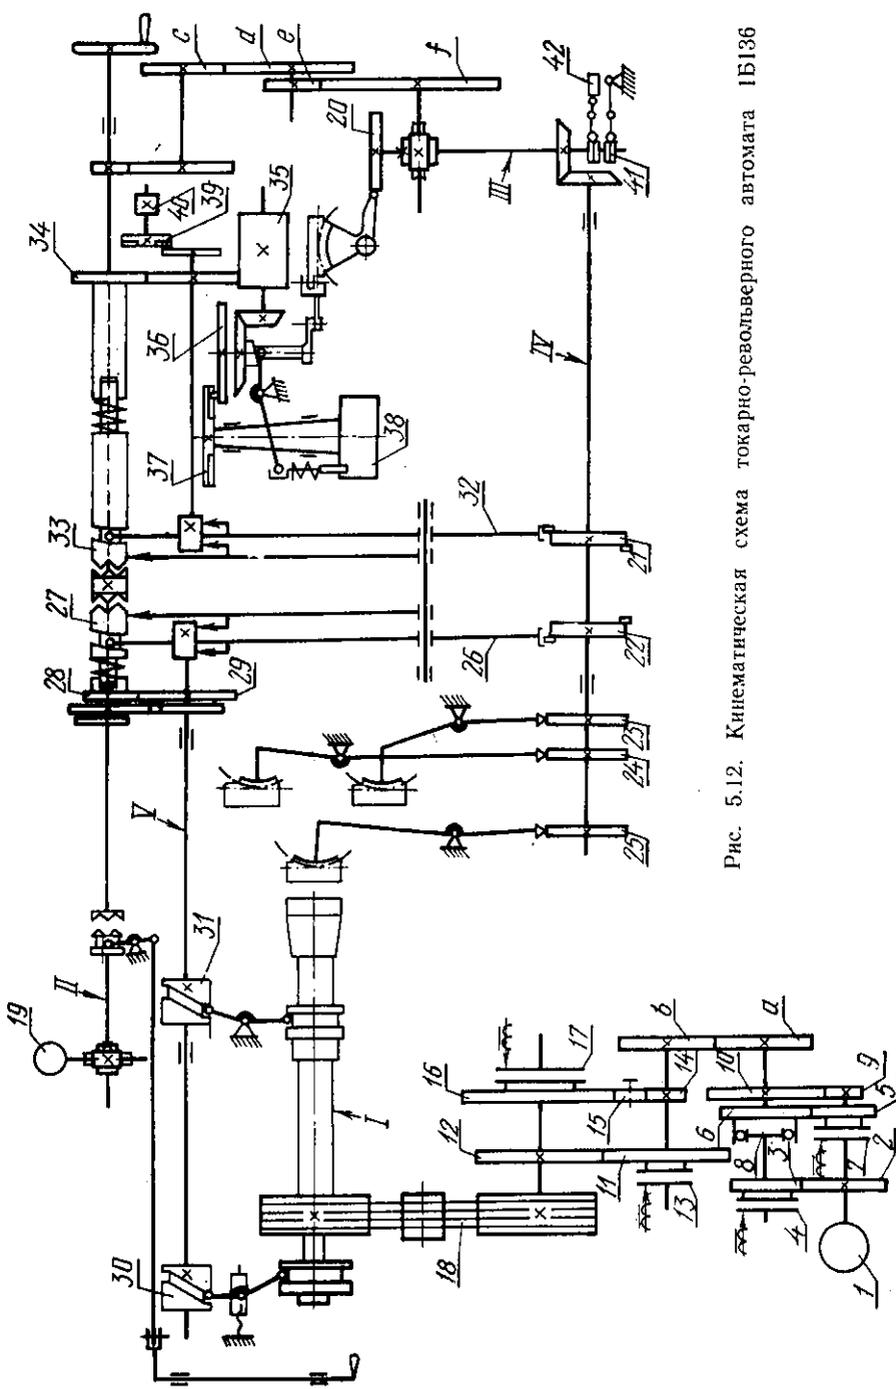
Кинематическая схема токарно-револьверного автомата 1Б136
